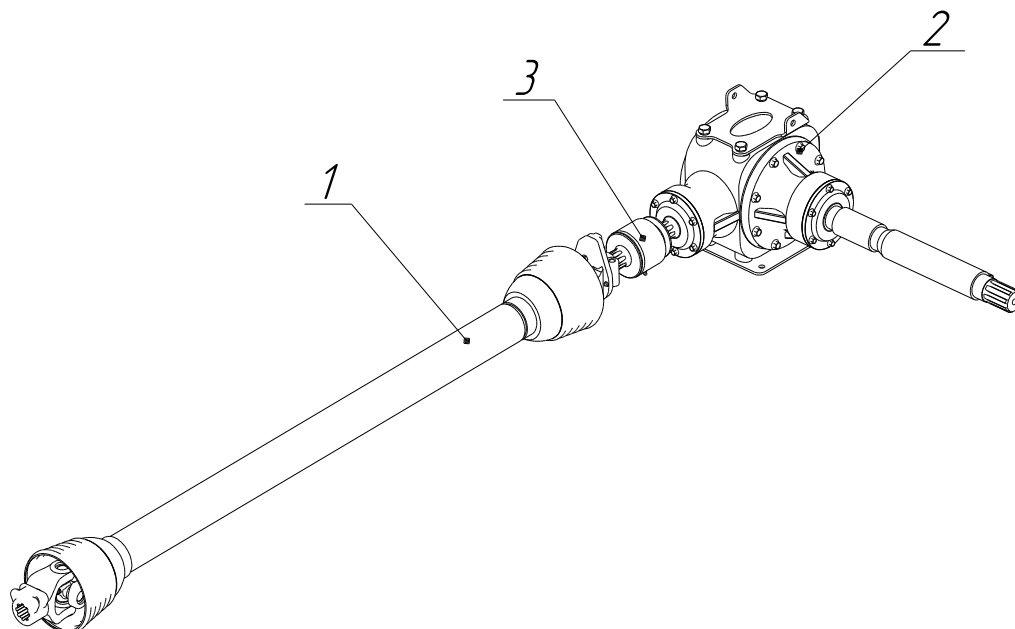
Привод пресс-подборщика: 1 – карданный вал; 2 - угловой конический редуктор с внутренним шлицевым рукавом; 3 – обгонная муфта.
